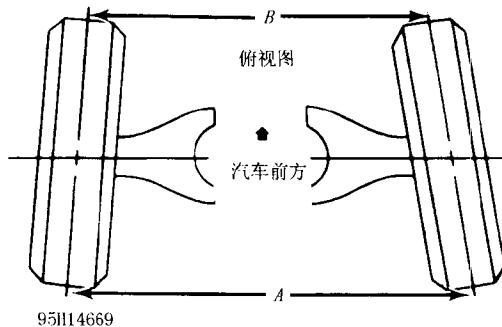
车轮前束(尺寸 A 减去尺寸 B)
